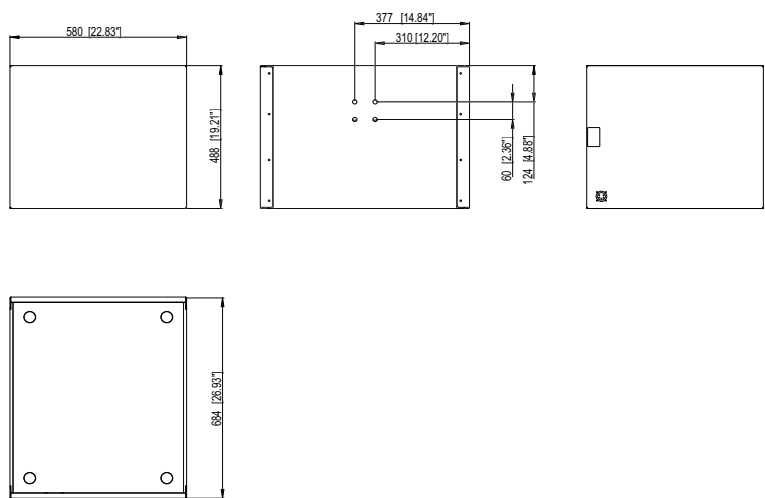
QiCSA-SUB dimensions du coffre en mm [inch]
